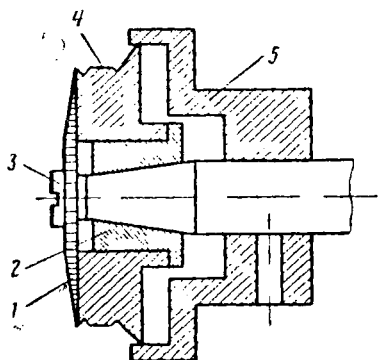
Фрезер, надетый на вал: 1—шайба, 2—наперсток, 3—винт, 4—фрезер, 5—патрон
